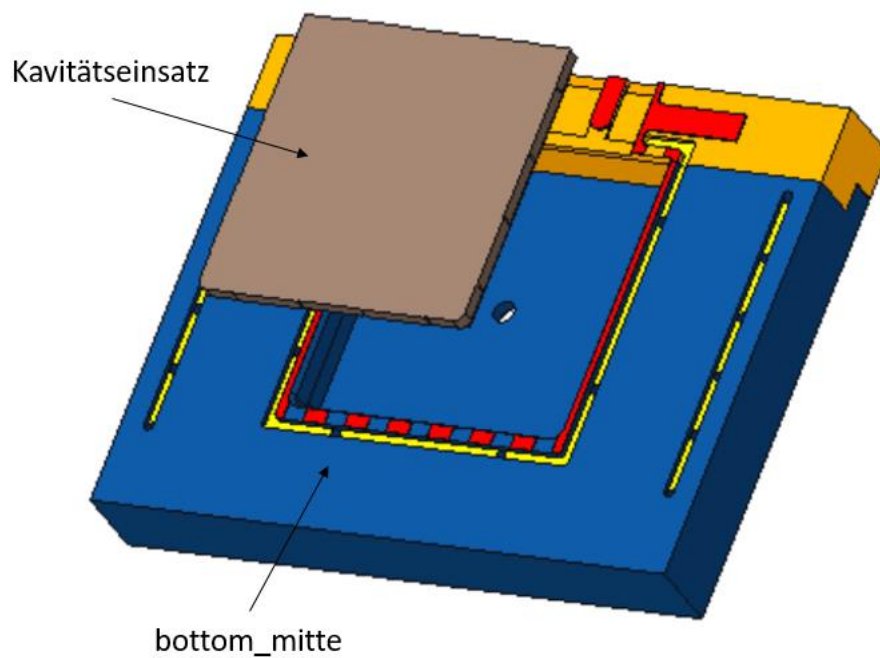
FAM-Werkzeug bottom\_mitte mit Kavitätsinsert
